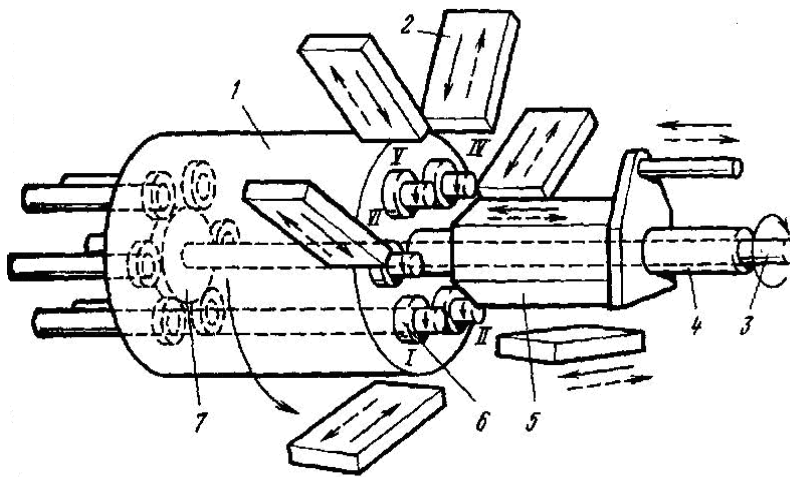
Схема роботи багатошпindelного токарного автомата
